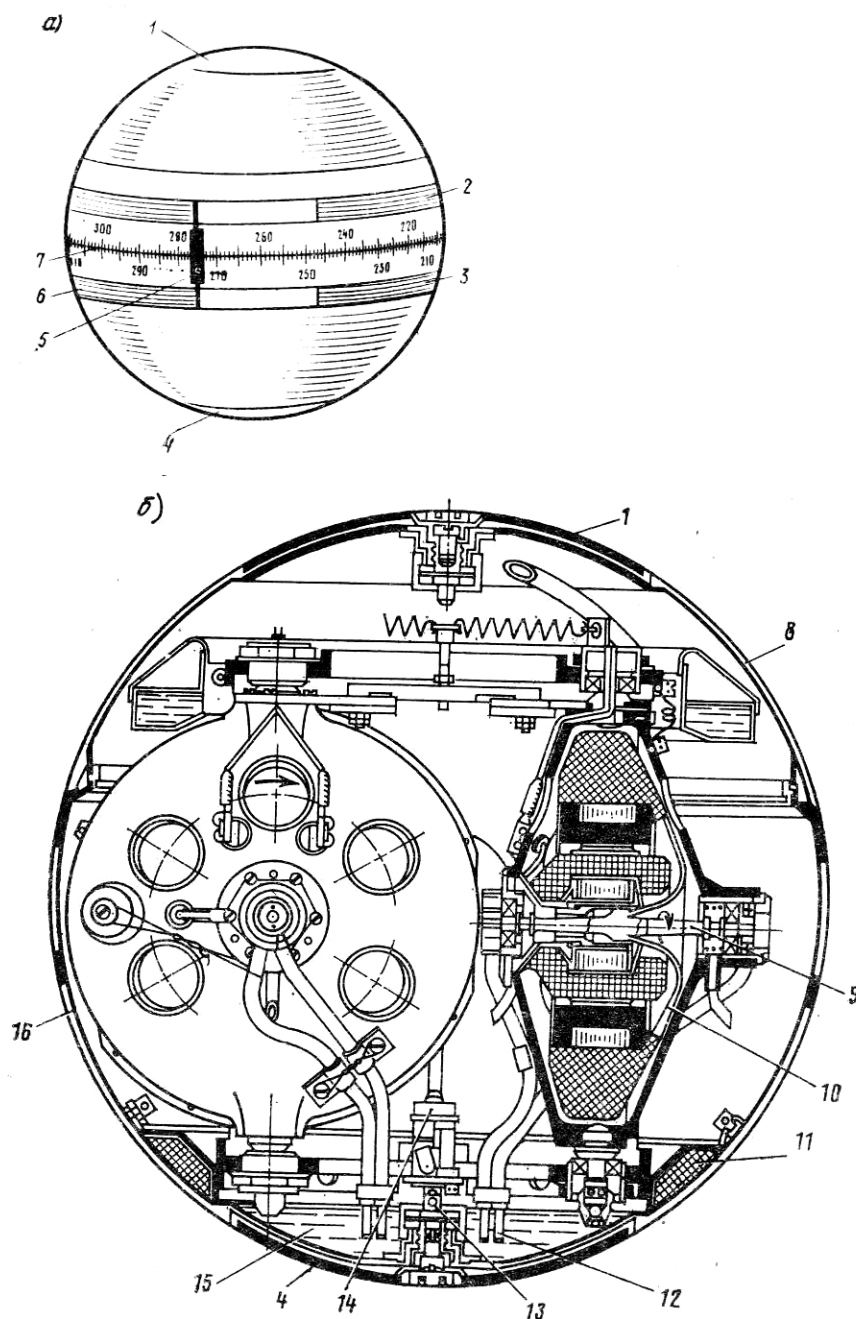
Гирисфера: а – внешний вид; б – корпус
